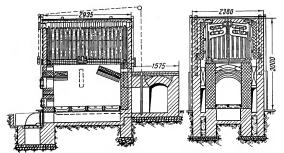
Габаритные размеры котла с поверхностью нагрева 43  $\mathit{m}^2$  с топкой для дров и торф а
